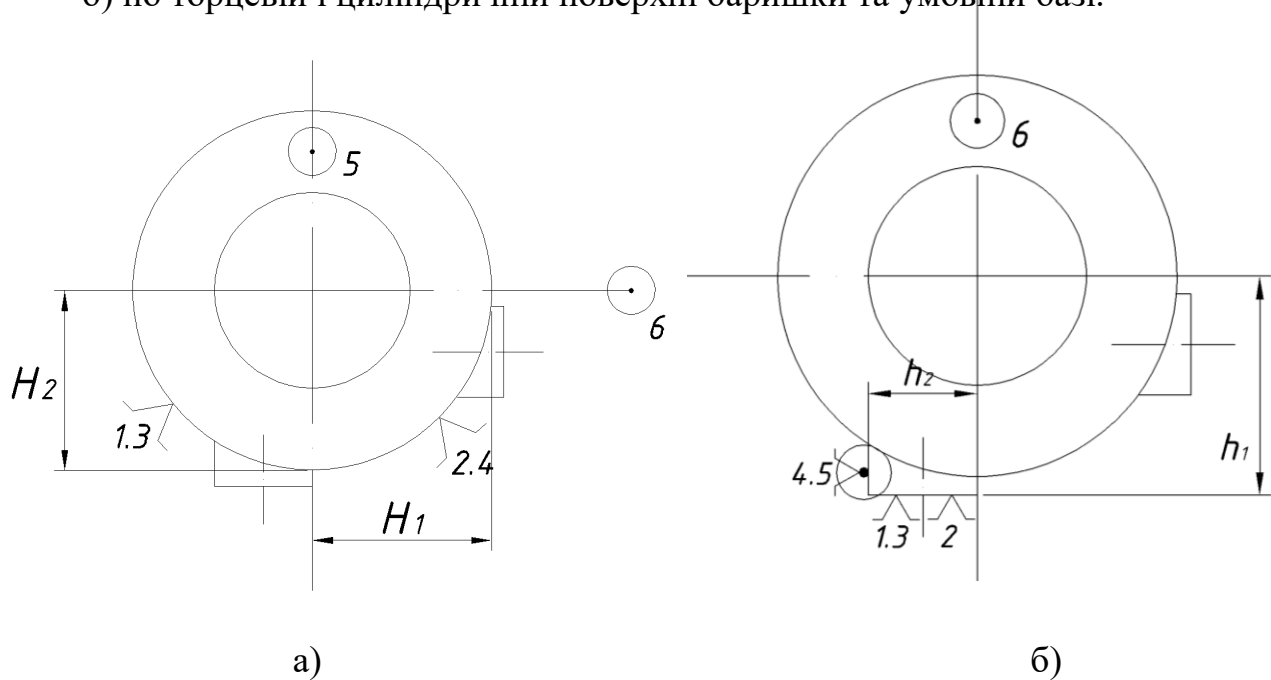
Варіанти базування заготовки корпусу:
